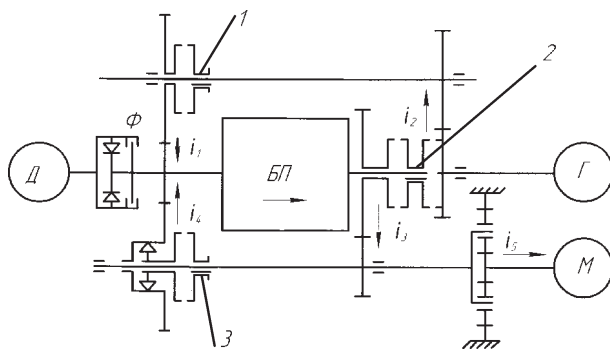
Кинематическая схема механической бесступенчатой передачи
